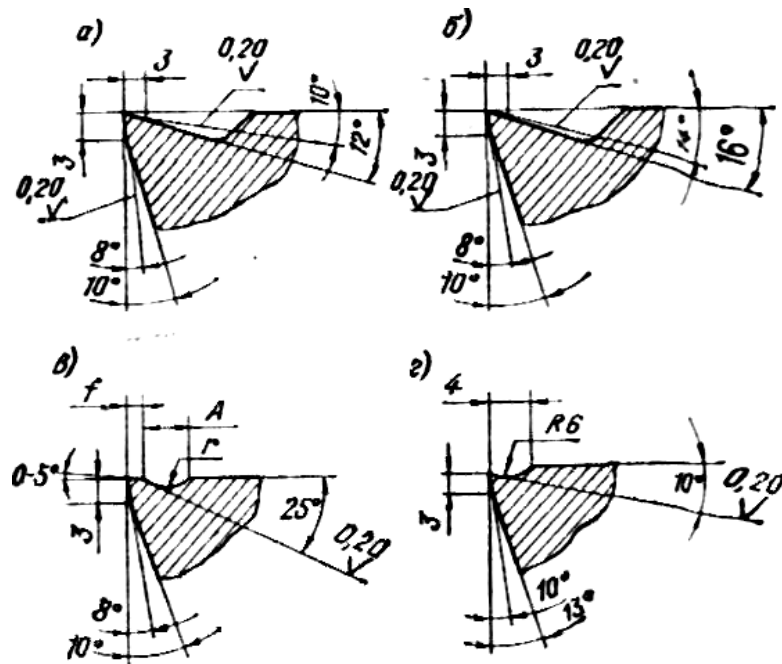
Форми заточування різців з швидкоріжучої сталі
